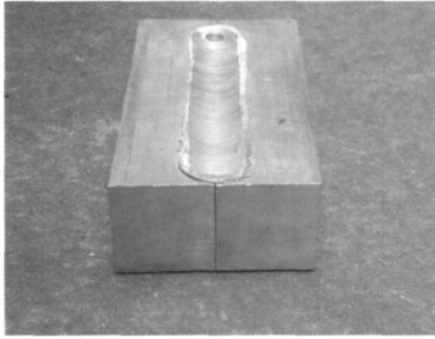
60mm 厚 6061-T6 铝合金厚板焊接
